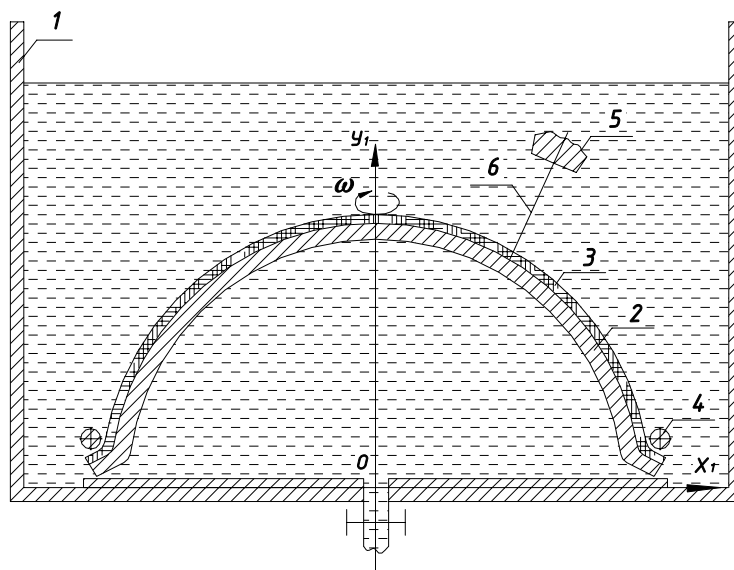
Схема експериментальної установки для формування деталей одягу гідроструминним способом: 1 – робоча камера; 2 – формуючий елемент; 3 – зразок тканини; 4 – притисне кільце; 5 – струменеформуючий насадок; 6 – занурений гідрострум; Ox_1y_1 – система координат, в якій розміщено формуючий елемент зі зразком тканини; ω – швидкість обертання формуючого елемента
